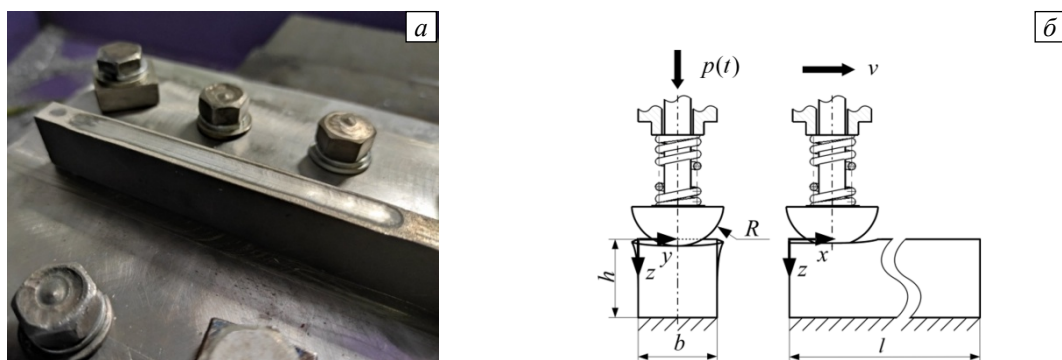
Контрольный образец, прокованный пневмомолотком, (а) и схема процесса проковки (б)
